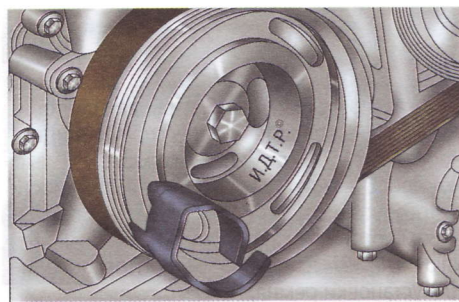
Установка приспособления для монтажа ремня привода компрессора кондиционера на шкив коленчатого вала
